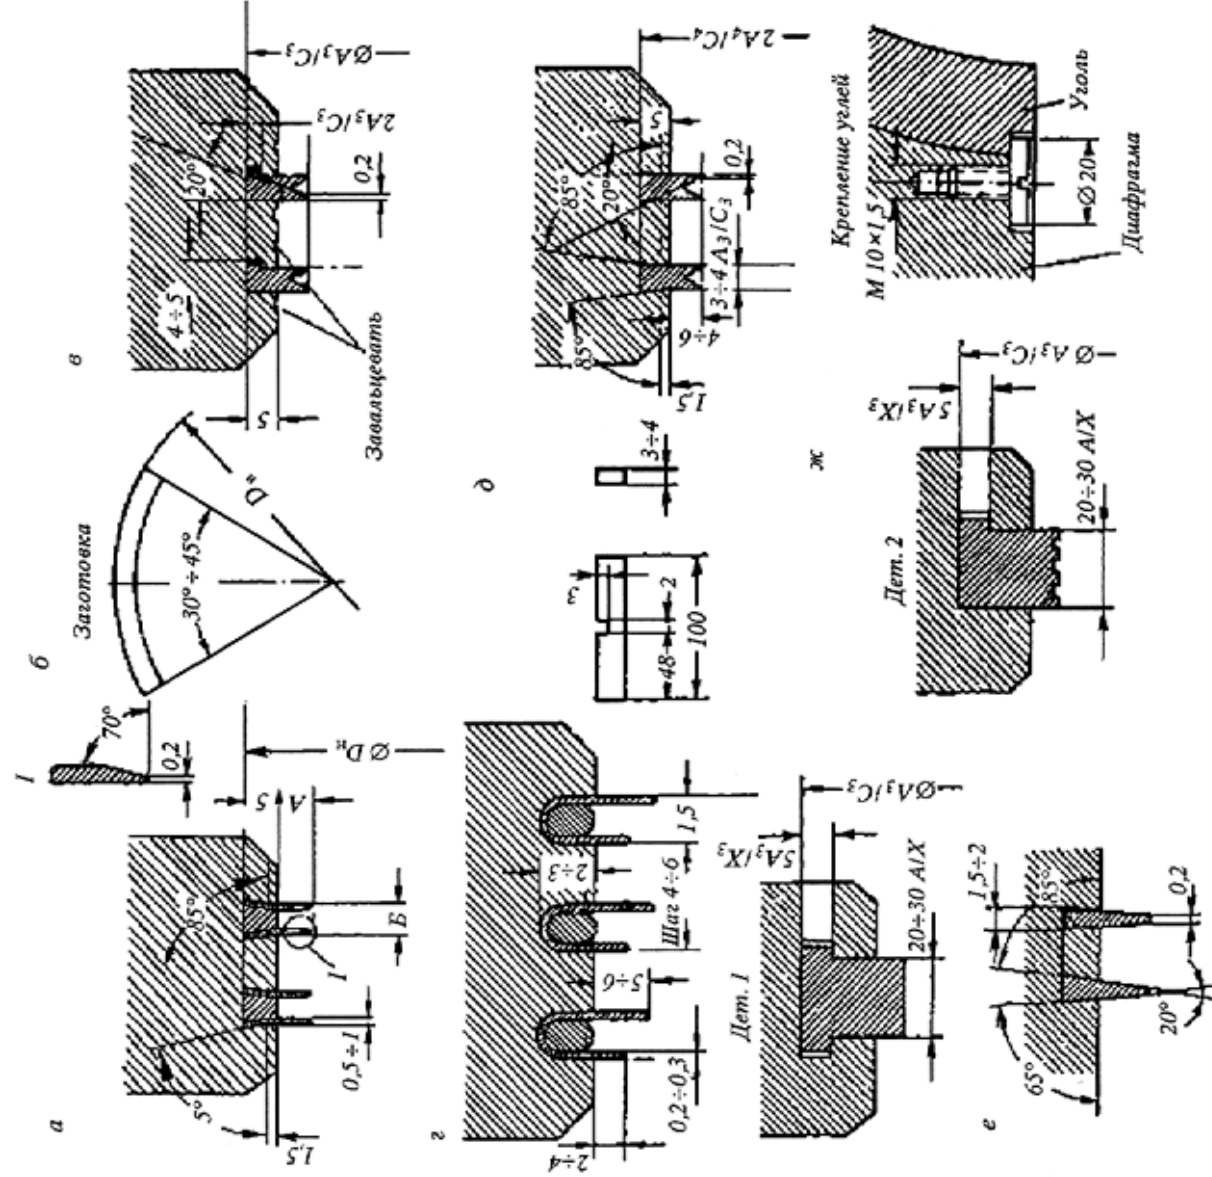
Конструкции наборных гребней уплотнений: а, г – установка тонких уплотняющих гребней с промежуточным телом; б – заготовка уплотняющего гребня; в, д, е – установка уплотняющего гребня, выполненного по ширине паза
